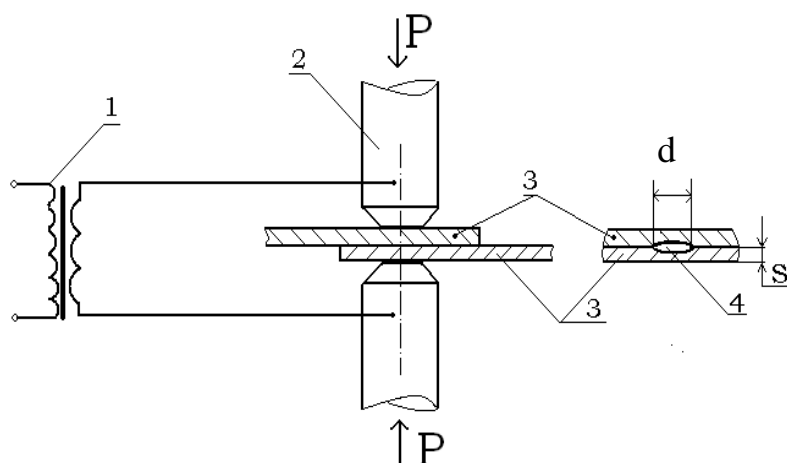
Схема процесса электроконтактной точечной сварки: 1-сварочный трансформатор; 2-электроды; 3-свариваемые заготовки; 4 –сварная точка;  $P$  – давление приложенное к электродам, [кН];  $d$  – диаметр сварной точки, [мм];  $S$  – толщина свариваемых изделий, [мм].
